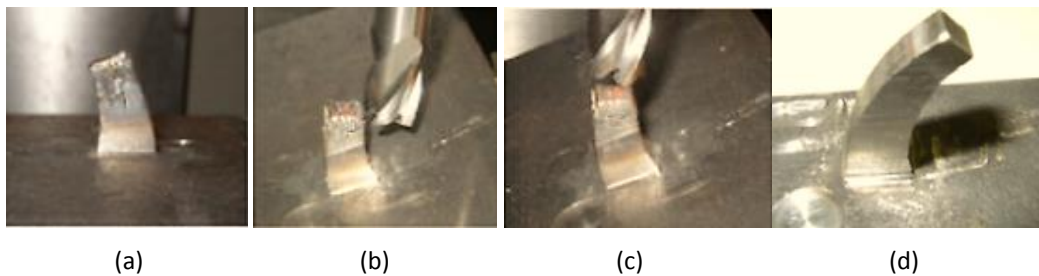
Proceso de fabricación de una pieza mediante DLD-CNC: (a) deposición de material, (b) fresado del contorno de la capa, (c) fresado de la superficie superior de la capa, (d) pieza final, [119].
